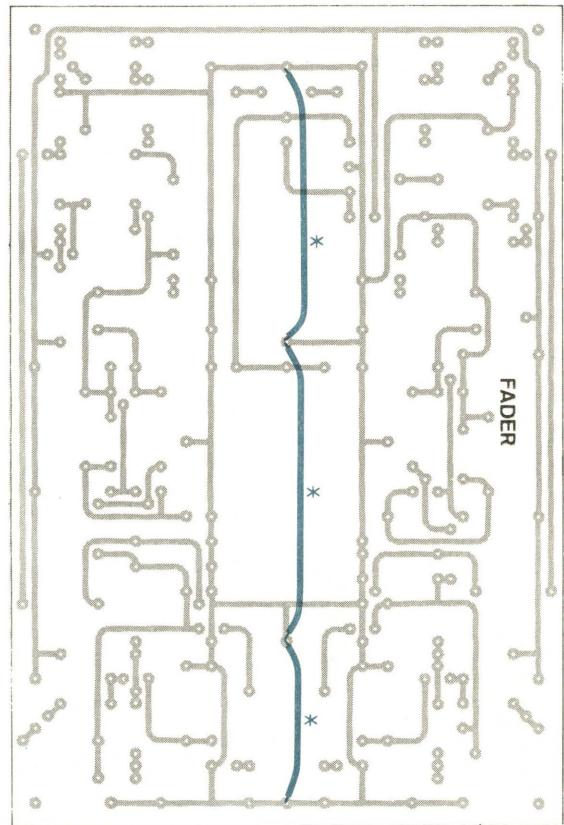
Si l'on constatait un léger ronflement, il conviendrait de placer côté soudure les straps comme sur le dessin.
